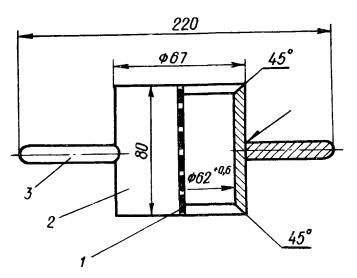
Приспособление для обжатия пакета уплотнения амортизатора (Ст. 3): I — шарнир; 2 — втулка разрезная; 3 — рукоятка
